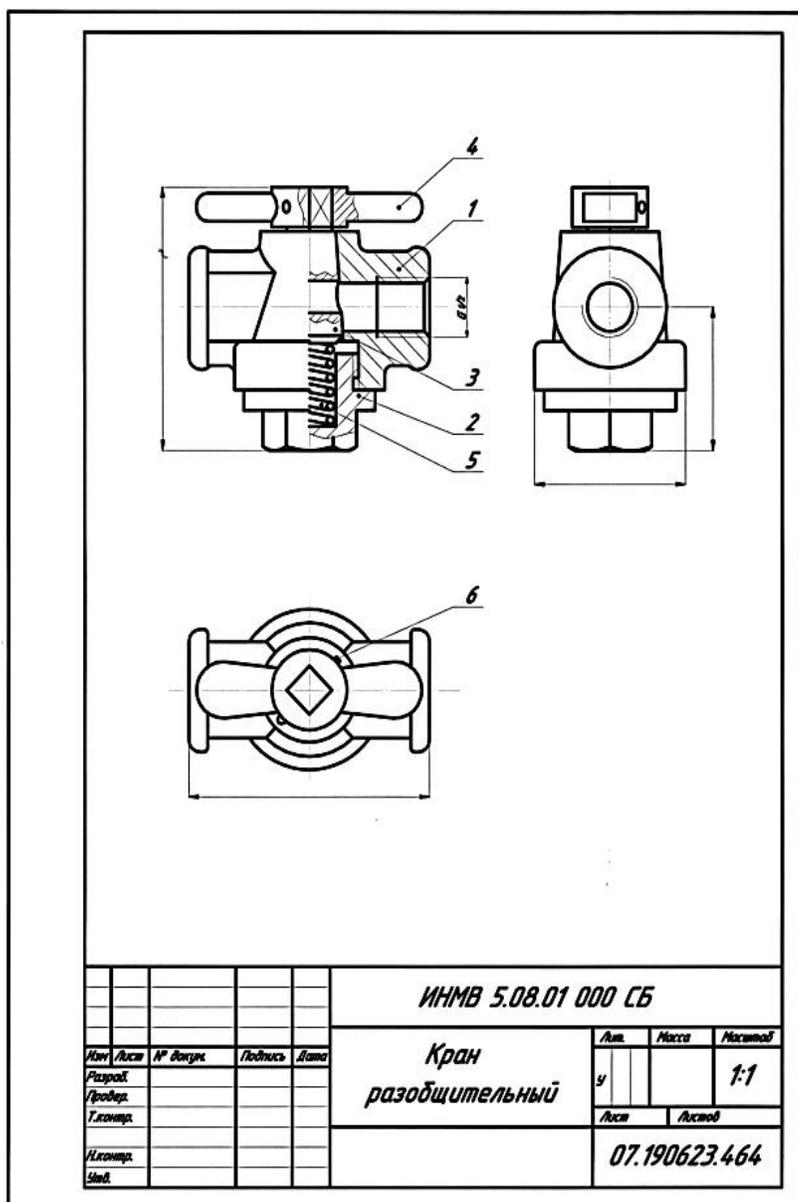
Образец сборочного чертежа для самостоятельной работы № 6 (вариант 1)
